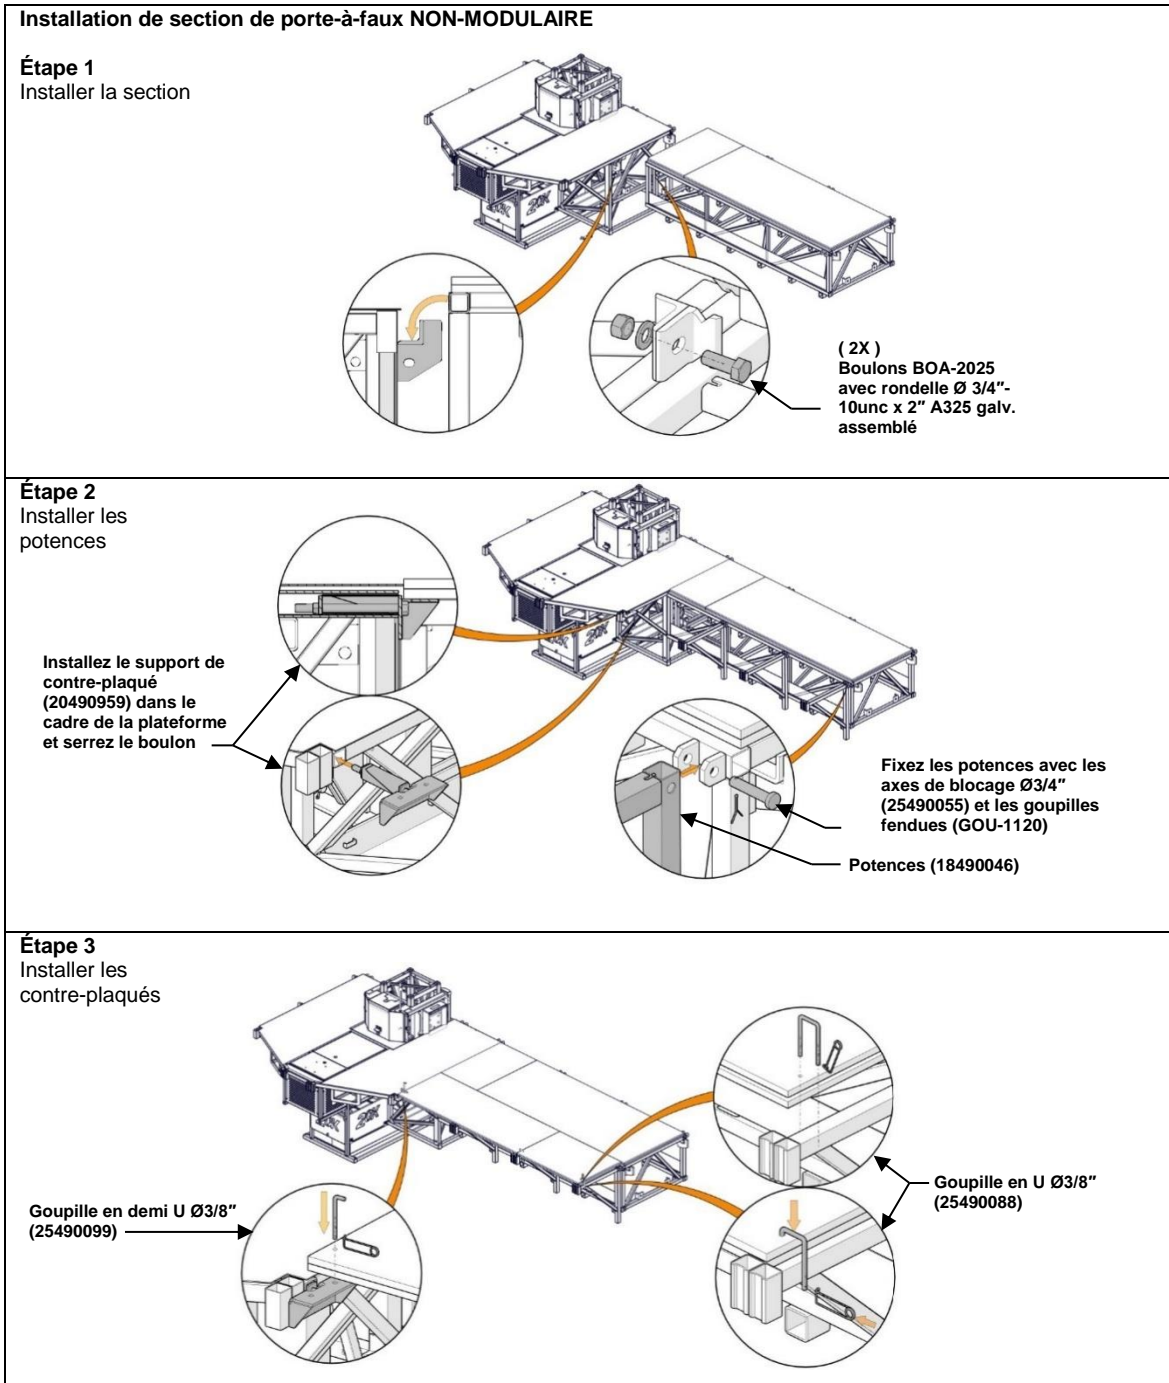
Section de porte-à-faux NON-MODULAIRE
